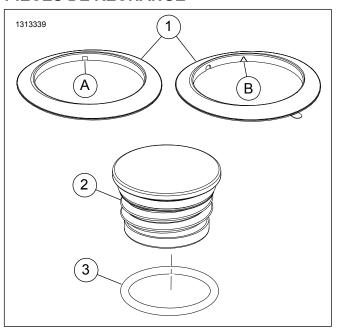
Pièces de rechange : Kit de bouchon de carburant encastré
